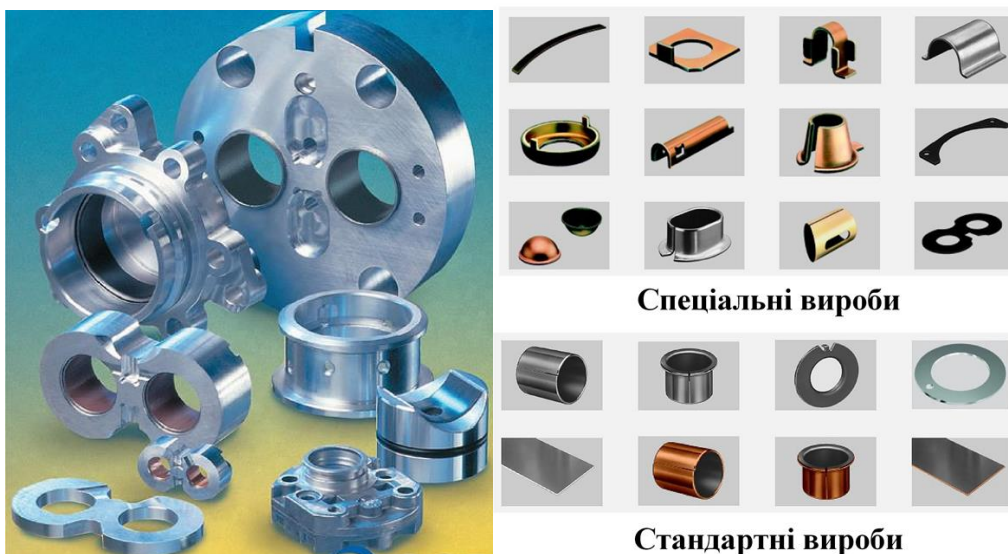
Метал-полімерні підшипники ковзання німецької компанії Glacier Garlock Bearings
